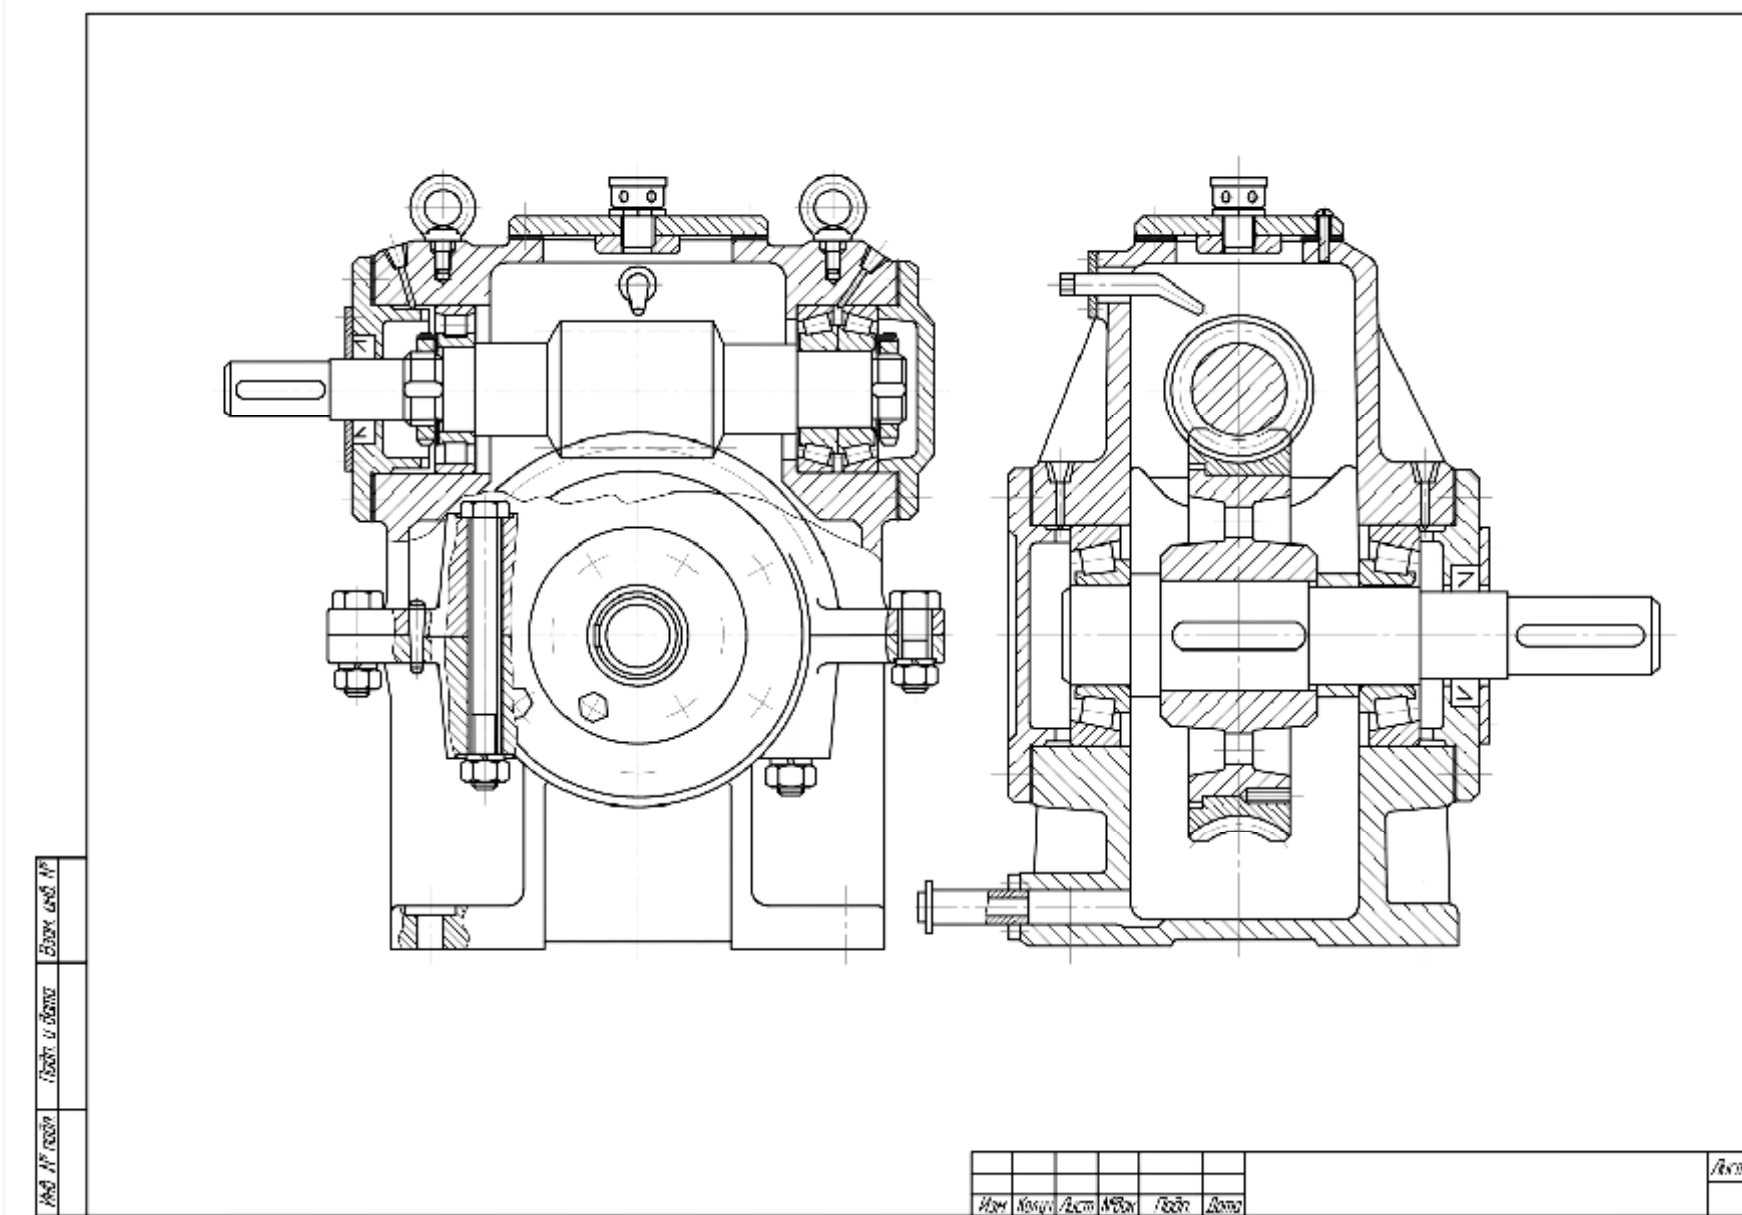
Редуктор червячный с верхним расположением червяка
